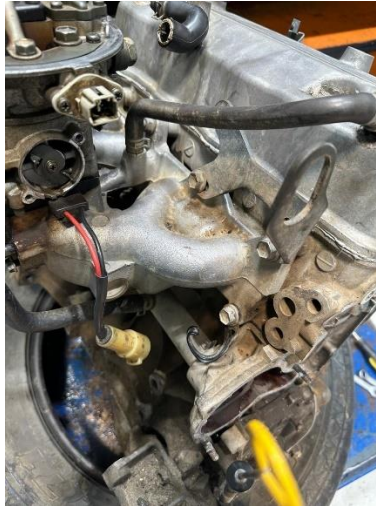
DESMONTAJE DE ALTERNADOR Y BOMBA DE AGUA
